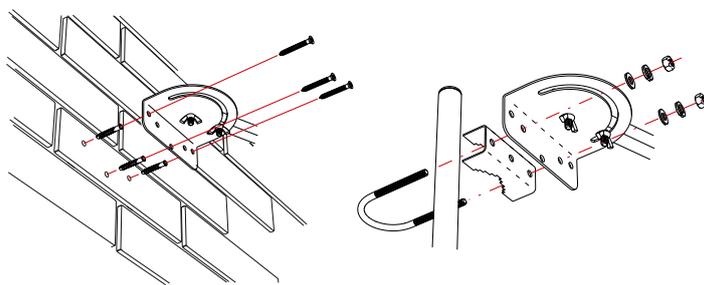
Монтаж установочного кронштейна на стену или мачту
